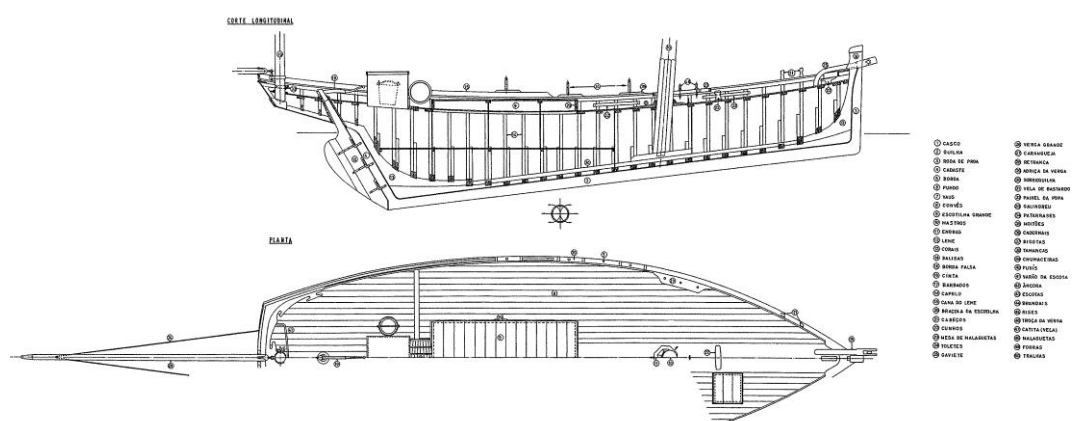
Vista de estrutura do casco em corte longitudinal e Planta
